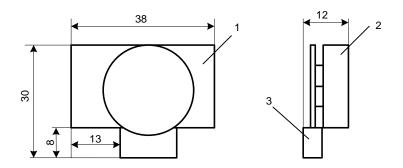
габаритные и установочные размеры преобразователя ЧИС
